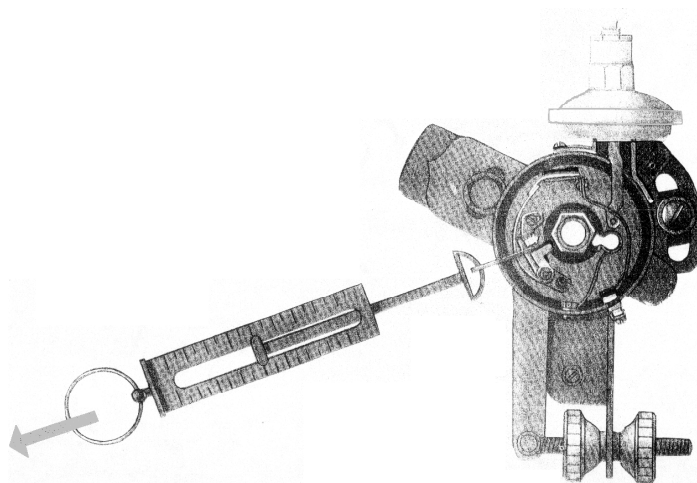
Схема проверки натяжения пружины контакта прерывателя.
